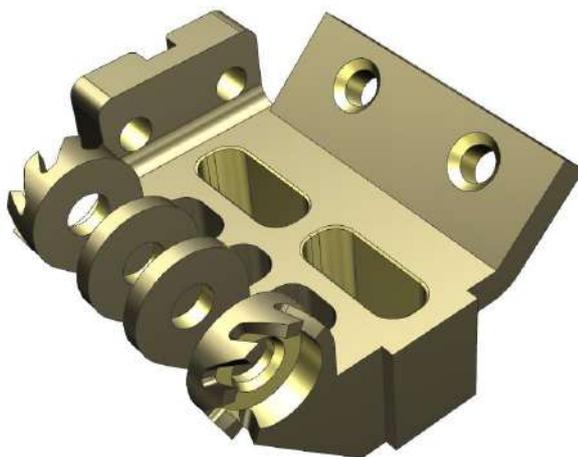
3D-модель изделия «Обойма», внешний вид
